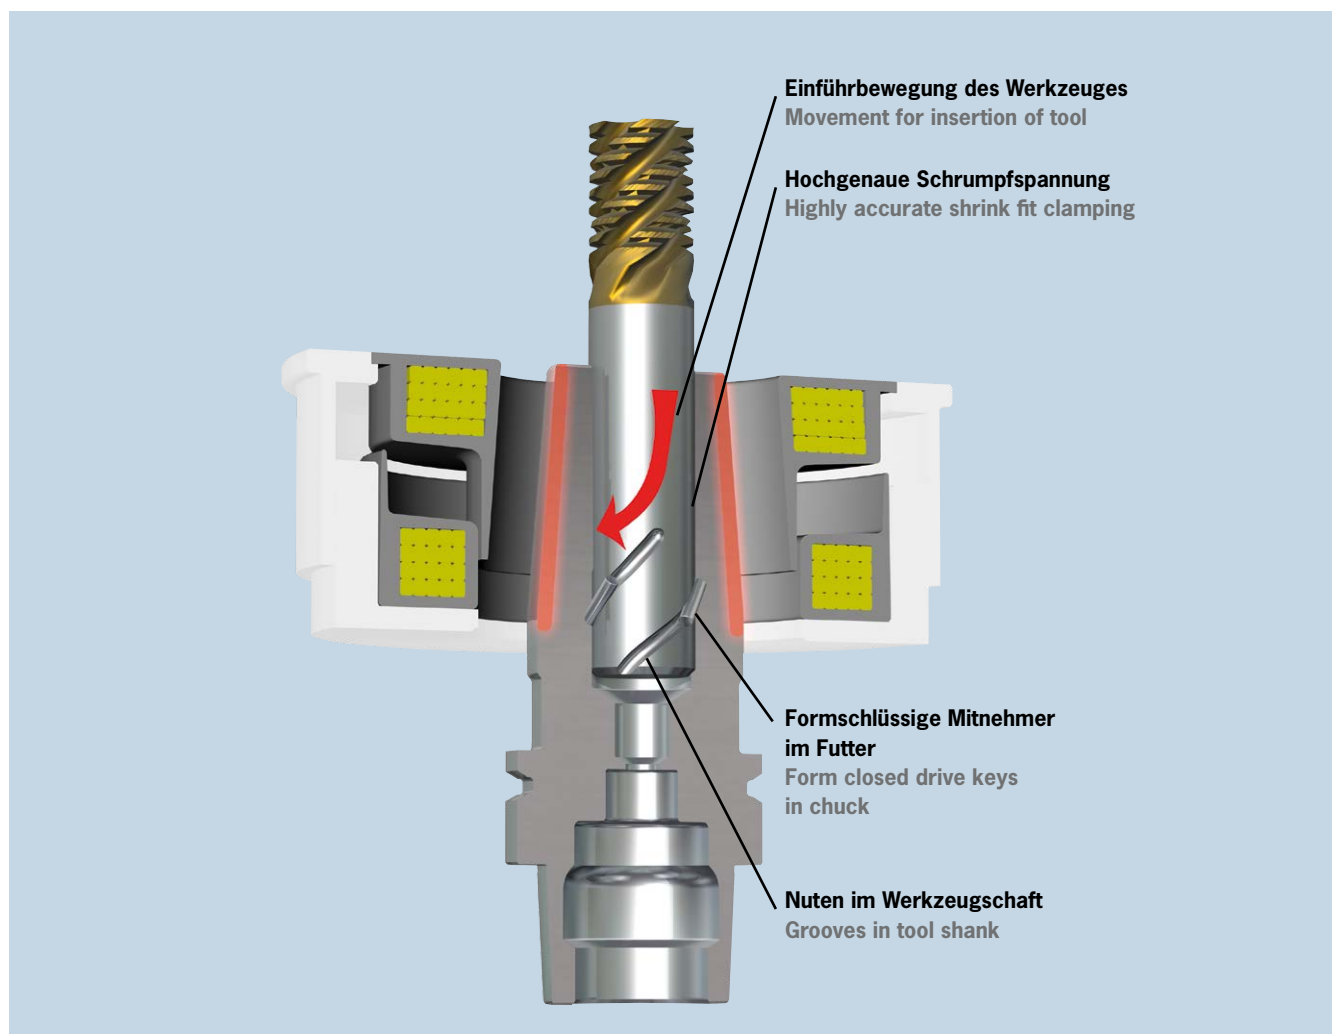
Mit Safe-Lock™ kein Werkzeugauszug
